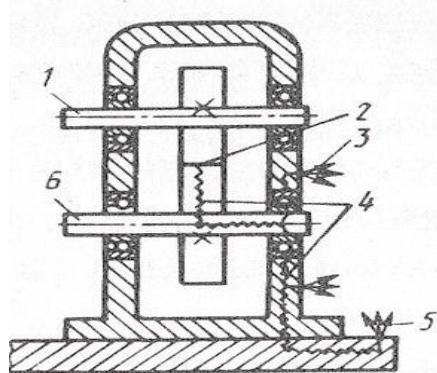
Схема передачі звуку в зубчастому приводі:
